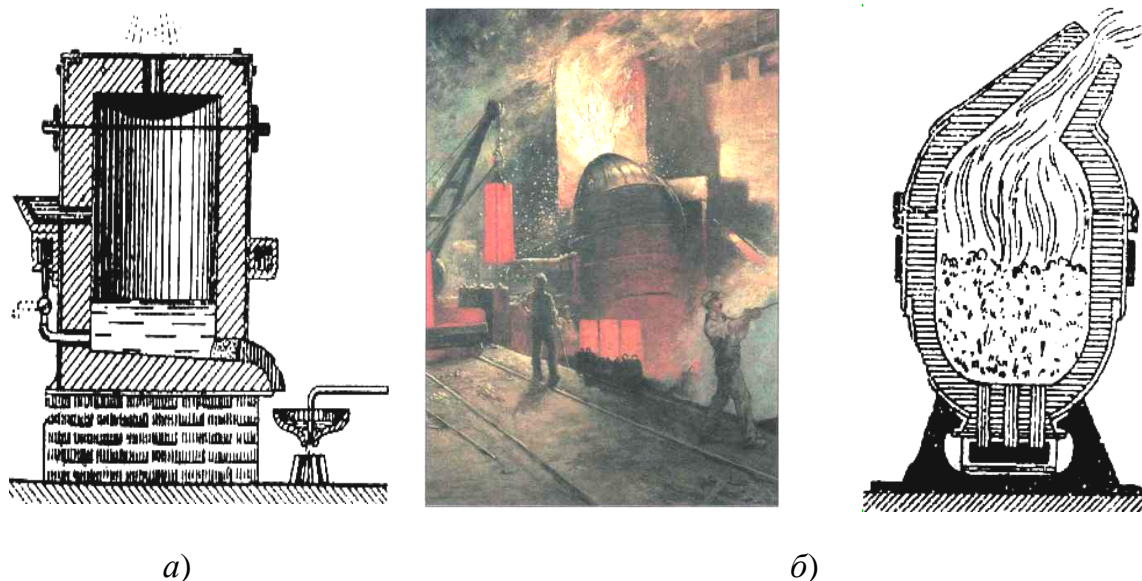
Схема опыта получения Бессемером литой стали в 1856 г. продувкой воздуха через металл, находившийся в тигле и помещенный в печь (а) и поворотный конвертер (б)
